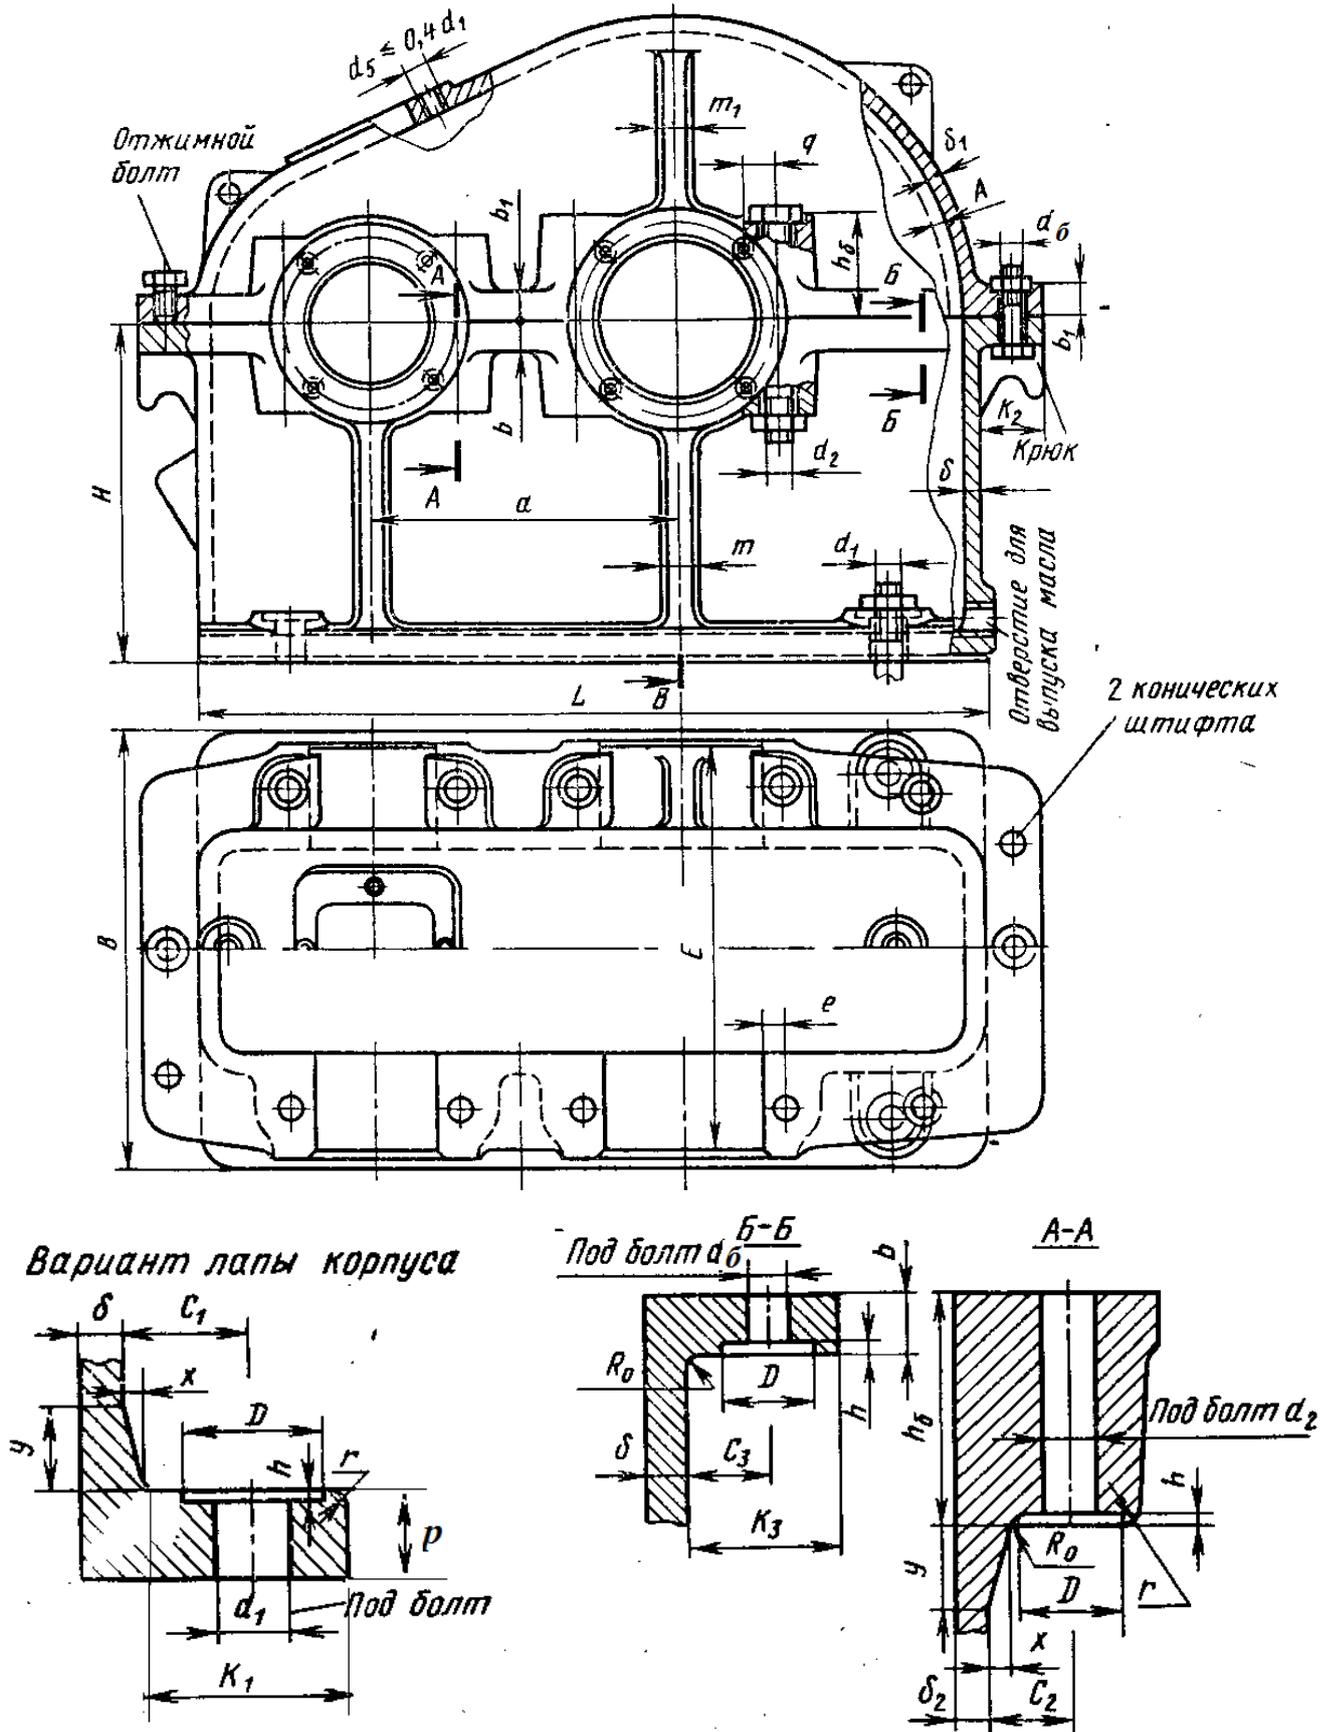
Конструктивные элементы литого корпуса редуктора
